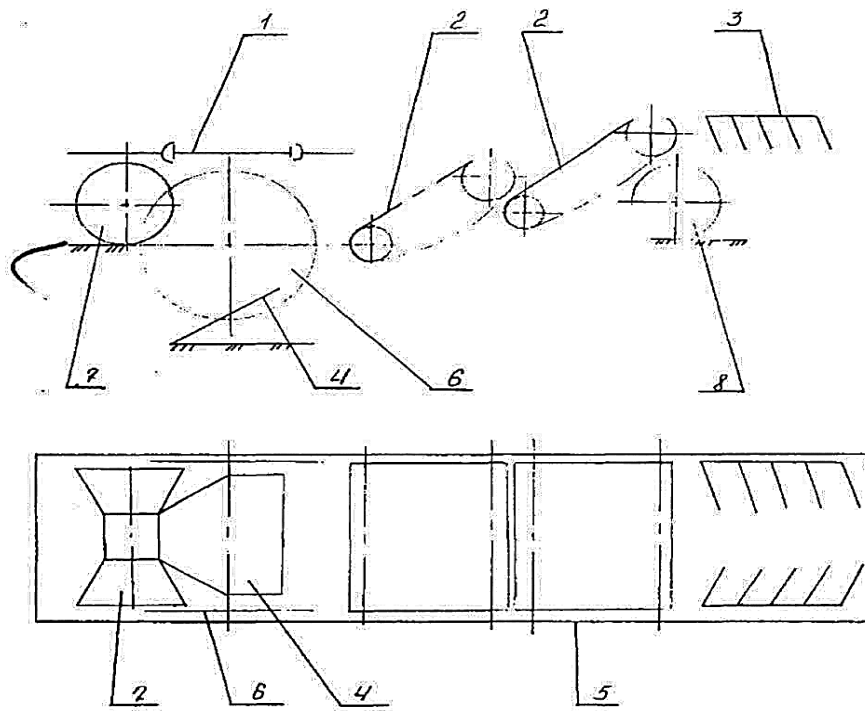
Конструктивна схема копача Л-651:1 – механізм привода копача; 2 – сепаратор; 3 – щитки для утворення валка; 4 – леміш; 5 – рама; 6 – обрізувальні диски; 7 – коток копій; 8 – пристрій для вирівнювання ущільнювальної дії на поверхню поля
